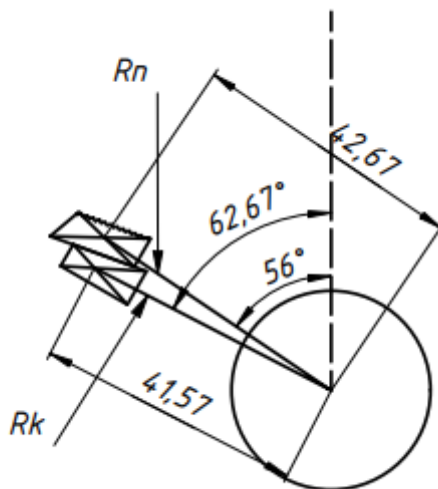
Схема зусиль затяжки гвинтом.
